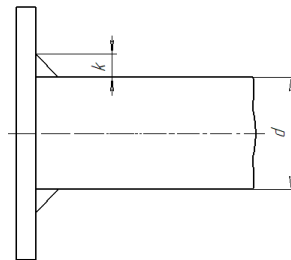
Зварного з'єднання (схематичне зображення).
